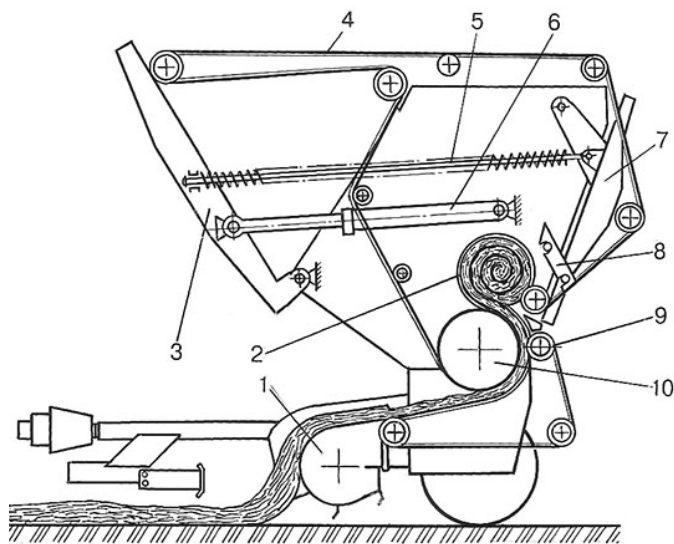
Технологическая схема работы рулонного пресс-подборщика с камерой прессования переменного объема: 1 – подбирающий аппарат; 2 – формируемый рулон; 3 – рамка; 4 – прессующий ремень; 5 – подпружиненная штанга; 6 – гидроцилиндр; 7 – клапан; 8 – защелка; 9 – транспортер; 10 – барабан
